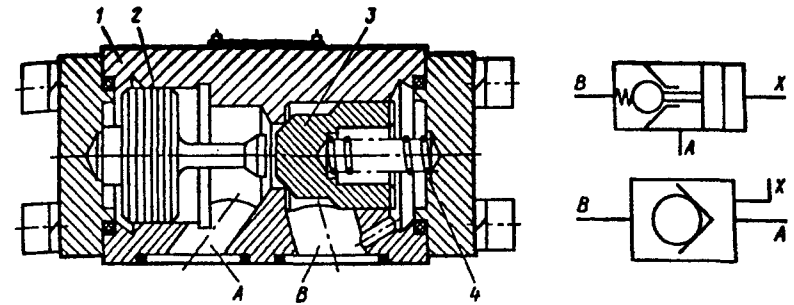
Односторонний конусный неразгруженный гидрозамок
